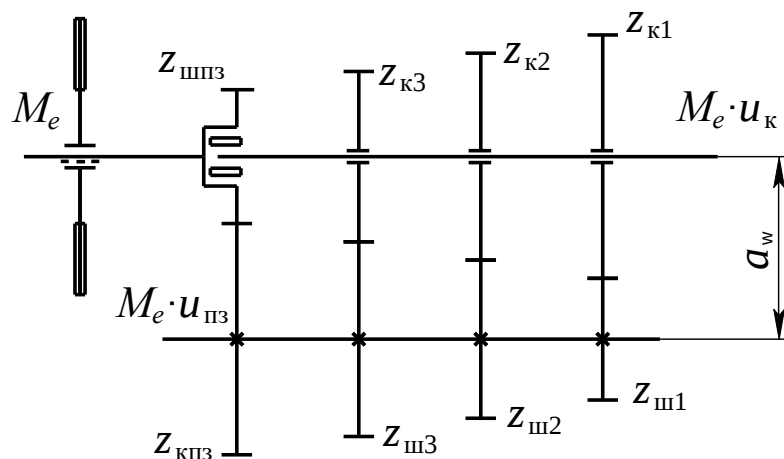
Розрахункова схема тривальної коробки передач:
